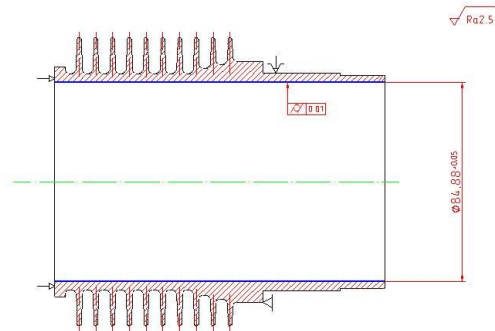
Эскиз обработки заготовки на отделочно-расточном станке 1Р-ТС95
